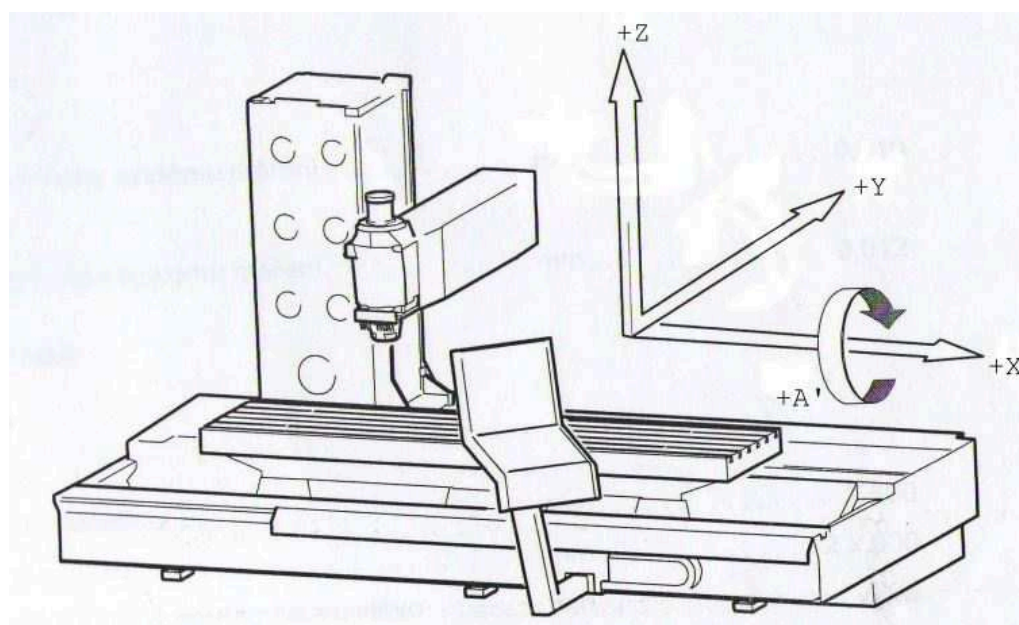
Obráběcí stroj DMF 250 linear (DMG) [10].
